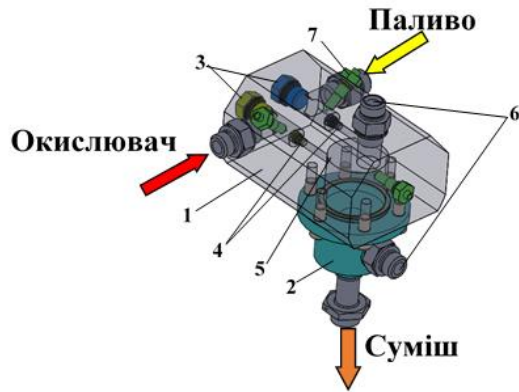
Модель змішувача 1 – корпус; 2 – кришка; 3 – корки; 4 – жиклери; 5 – камера змішувача; 6 – штуцери; 7 – датчики
